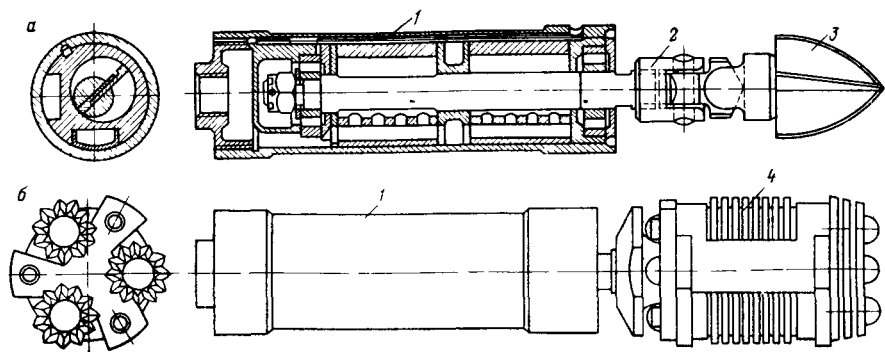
Приспособление для механической чистки внутренних поверхностей труб бойком (а) и шарошкой (б)
